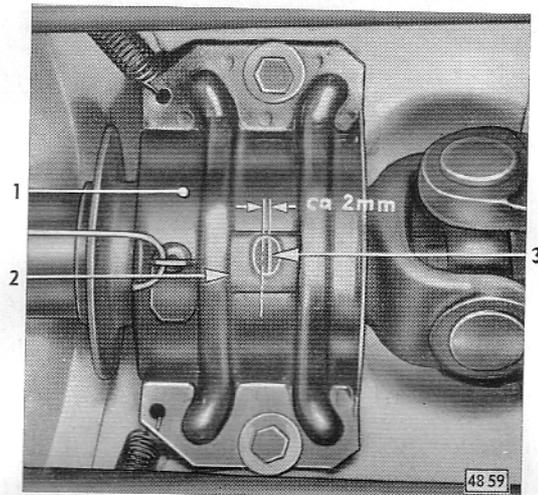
Führungshülse für Zwischenlager verspannt befestigt
